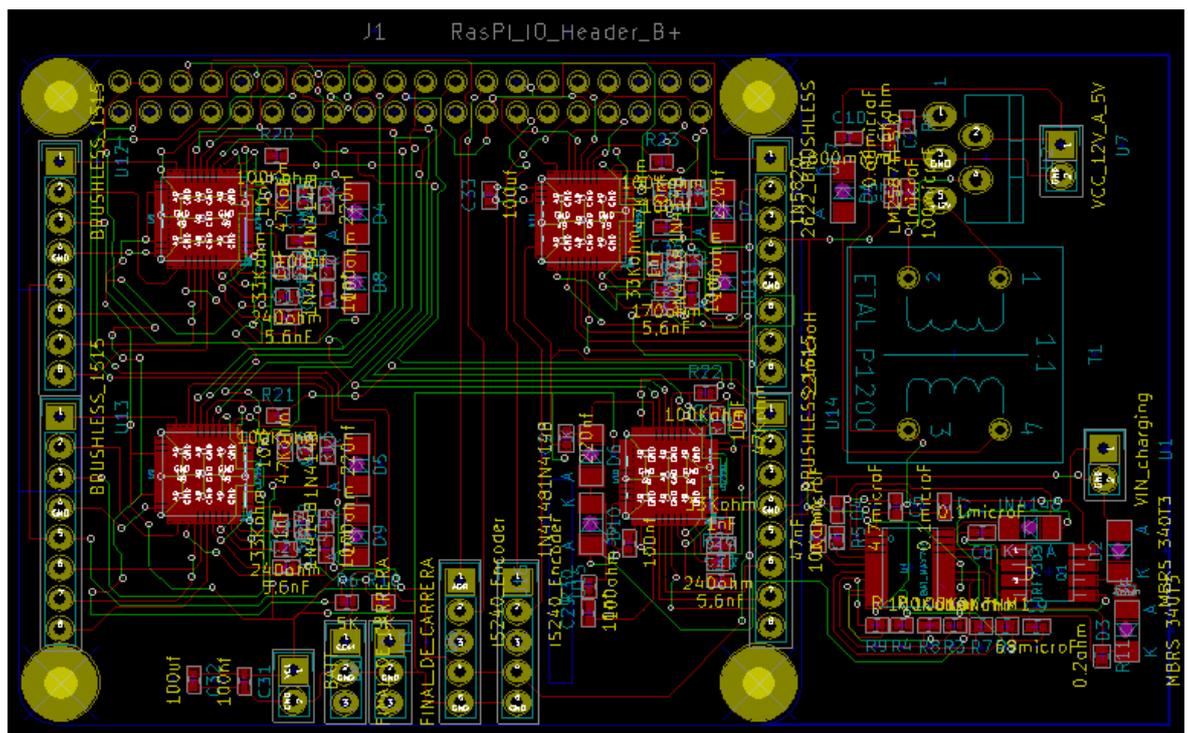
PCB de la etapa de potencia, kicad, diseño propio
